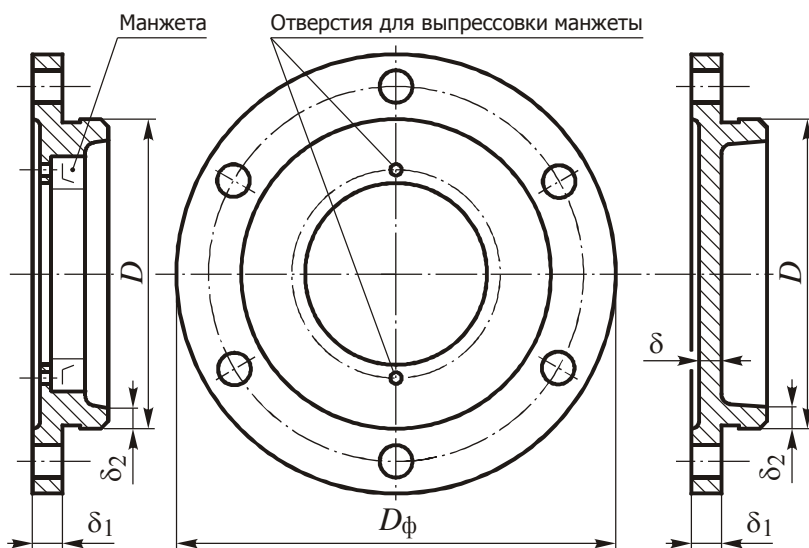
Крышки подшипников: слева – сквозная, справа – глухая
